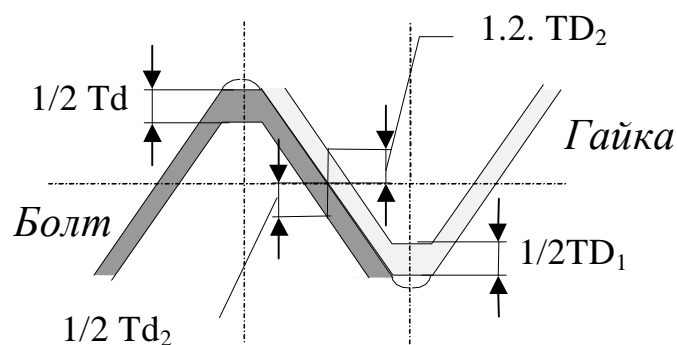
Розташування полів допусків зовнішньої та внутрішньої різьб
